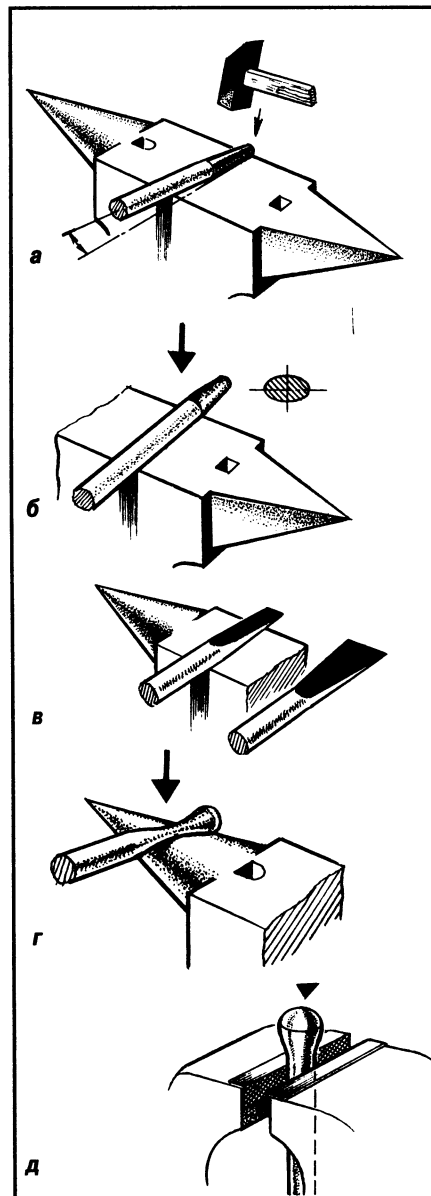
Ковка чеканов: а — протяжка ударной части «на конус»; б — протяжка остова «на эллипс»; в — ковка рабочей части; г — формирование шейки; д — «высадка» рабочей части.
